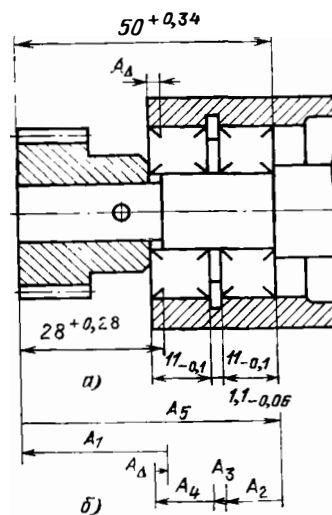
К расчету размерной цепи: а — узел вала с шарикоподшипником; б — схема размерной цепи
